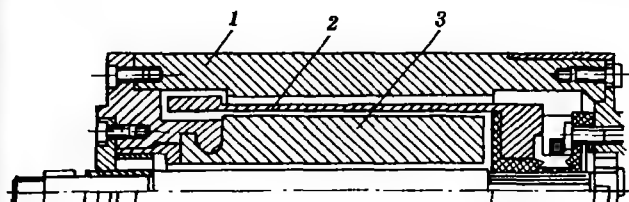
Двигатель серии ДПР с полым цилиндрическим якорем
